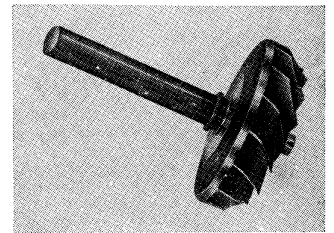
Ротор турбоагрегата. Сварка трением. Колесо из жаропрочной аустенитной стали, вал — из перлитной стали. Диаметр в месте сварки 20 мм.
